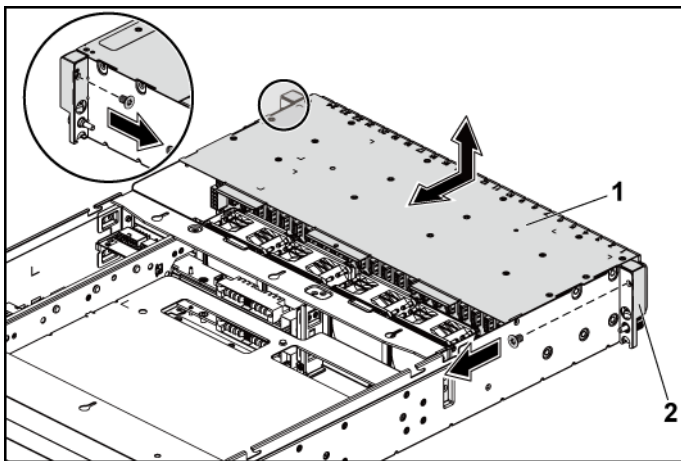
Retrait et installation du bâti de disque dur de 2,5 pouces (1)
